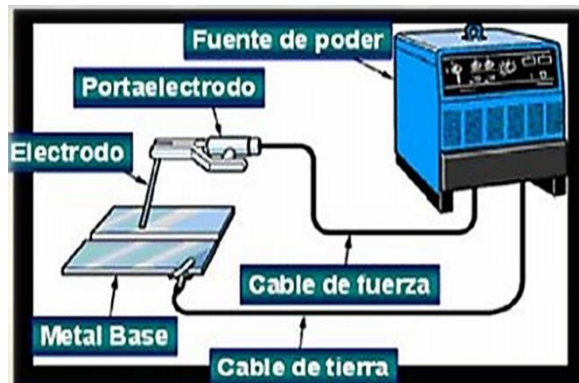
Diagrama del equipo de soldadura SMAW [31].
